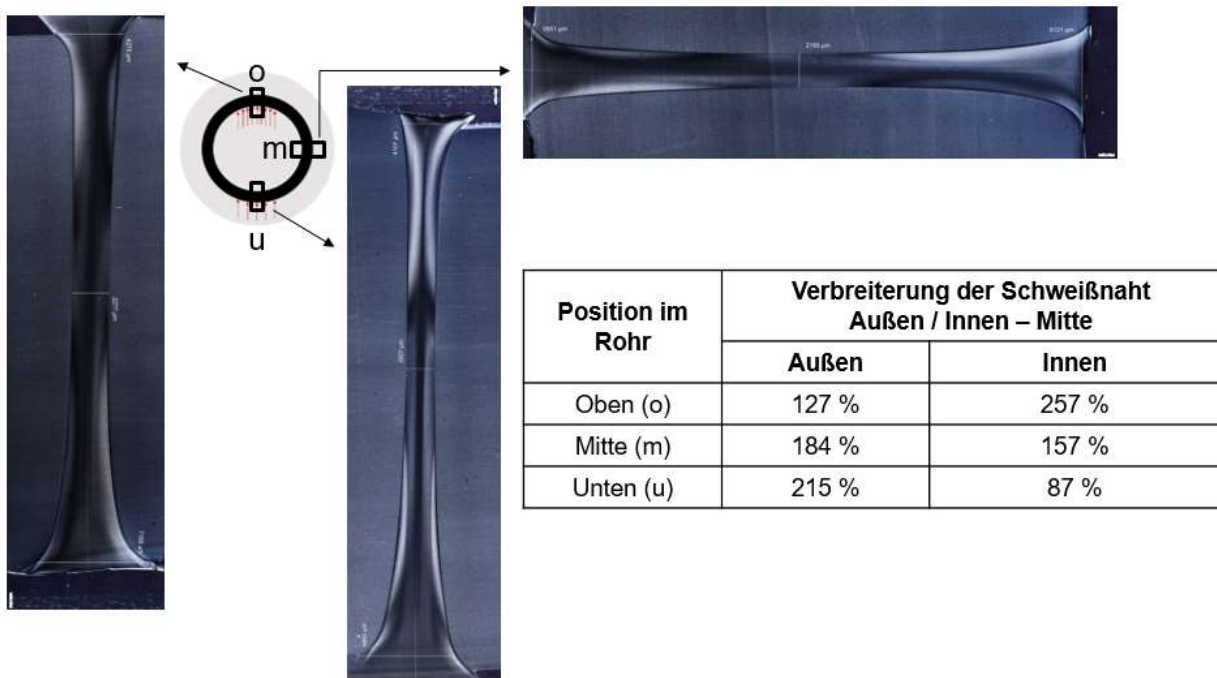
Mikroskopieaufnahmen eines geschweißten Rohres mit aufgrund der Seiteneinstrahlung und des Wärmestaus unterschiedlich ausgeprägten Schweißnahtkrümmungen
